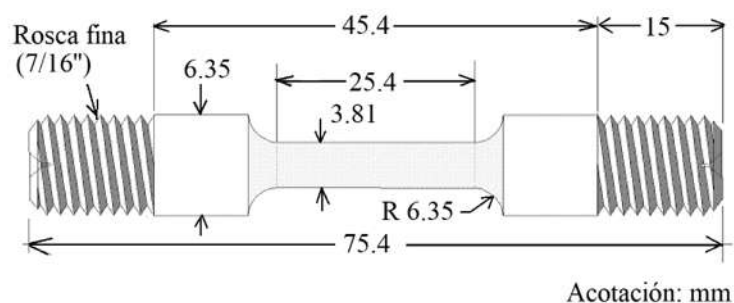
Dimensiones de probeta maquinada para prueba SSR [48].
